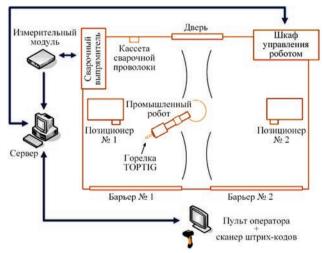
Планировка поста роботизированной сварки TOPTIG с системой контроля параметров сварки
